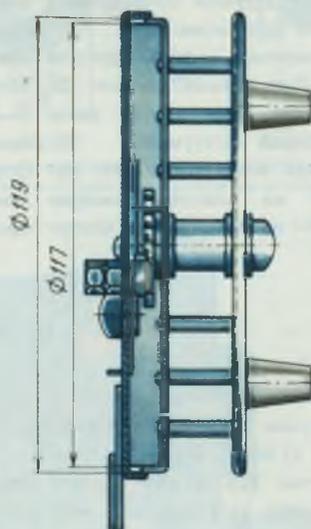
Корпус катушки с тормозным узлом в разрезе.
